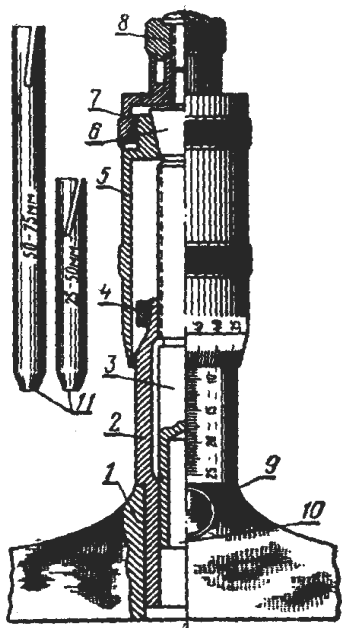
Микрометрический глубиномер: 1 – основание (траверса); 2 – стебель; 3 – микровинт; 4 – регулировочная гайка; 5 – барабан; 6 – хвостовик винта; 7 – установочный колпачок; 8 – трещоточное устройство; 9 – стопорный винт; 10 – отверстие для установки стержня; 11 – стержни
